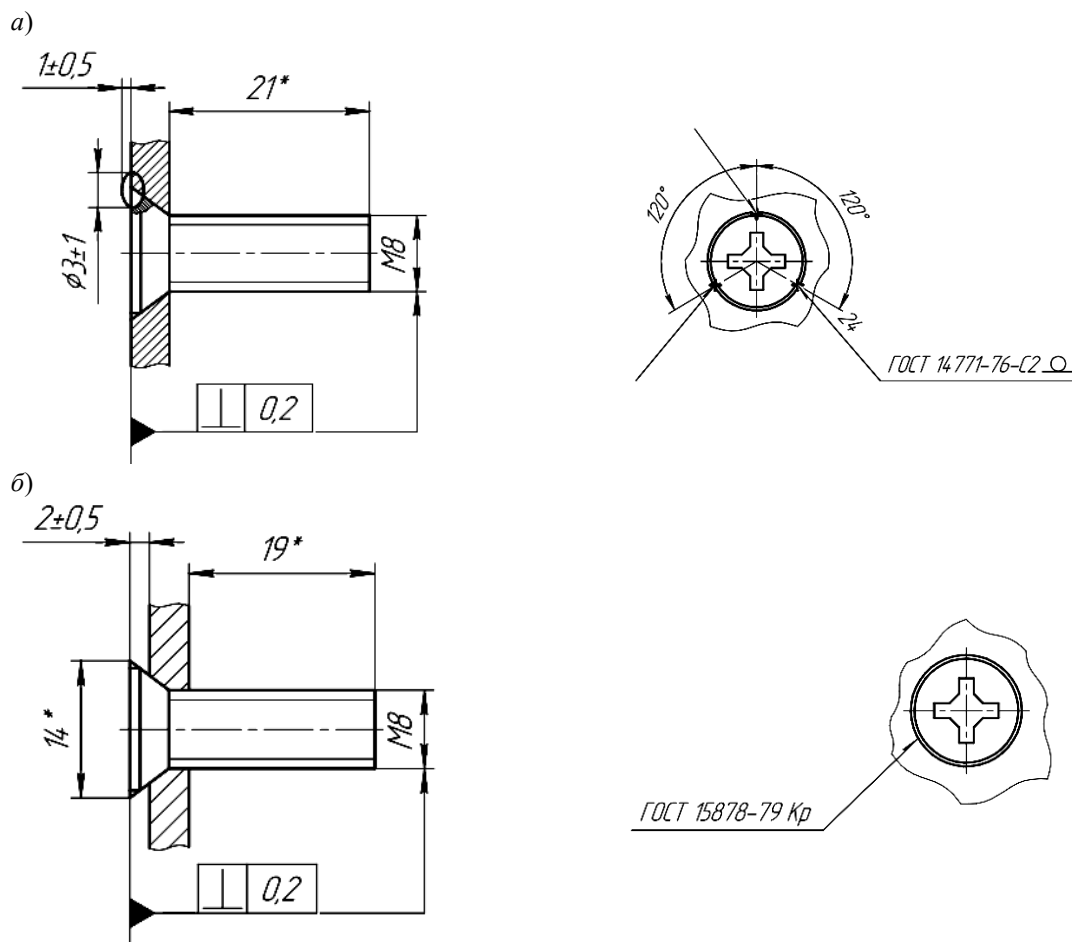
Соединение винта с пластиной из горячекатаной стали механизированной дуговой сваркой (а) и рельефной сваркой «острой гранью» (б)
